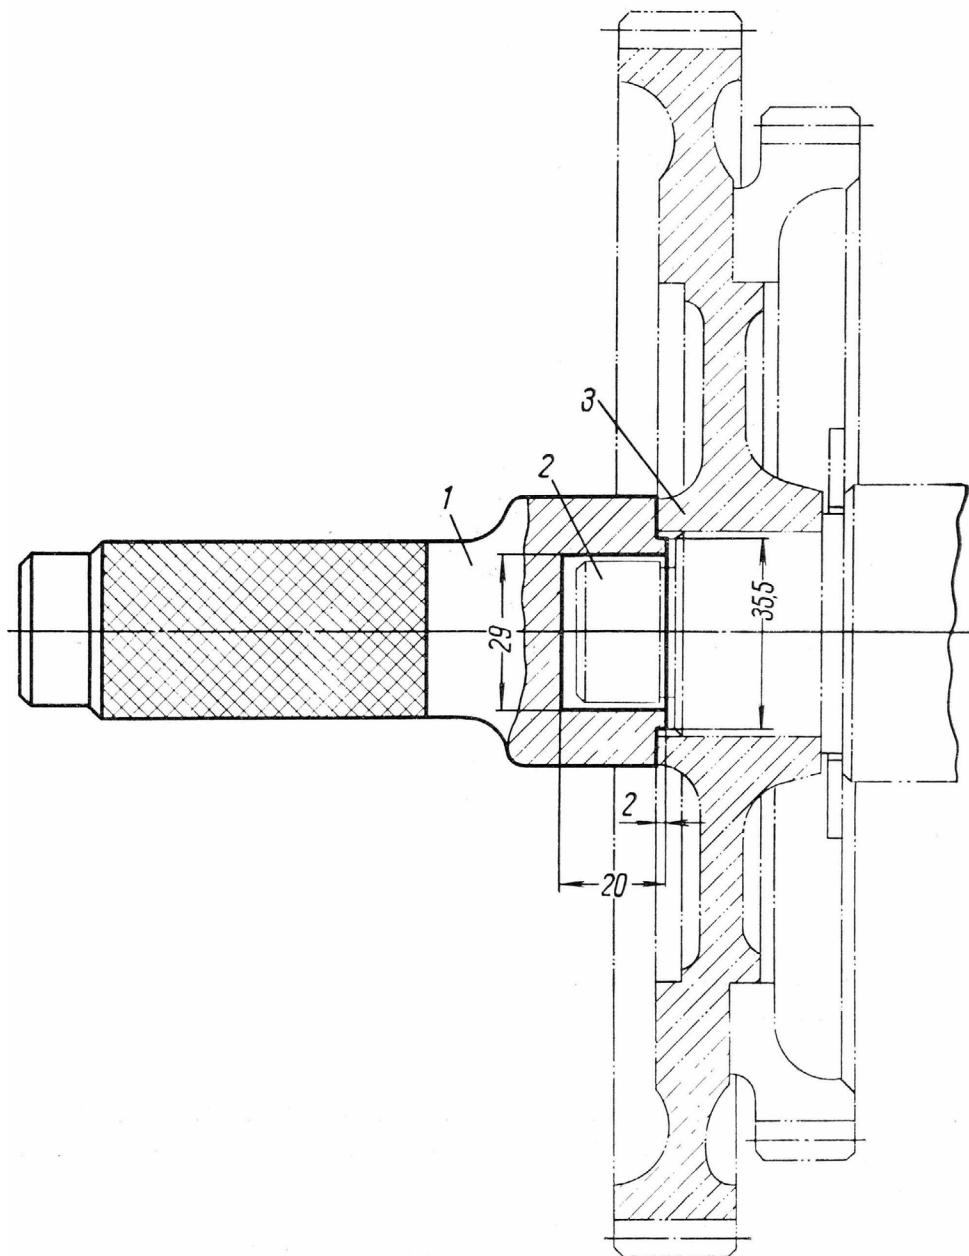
Оправка для напрессовки шестерни распределительного вала
